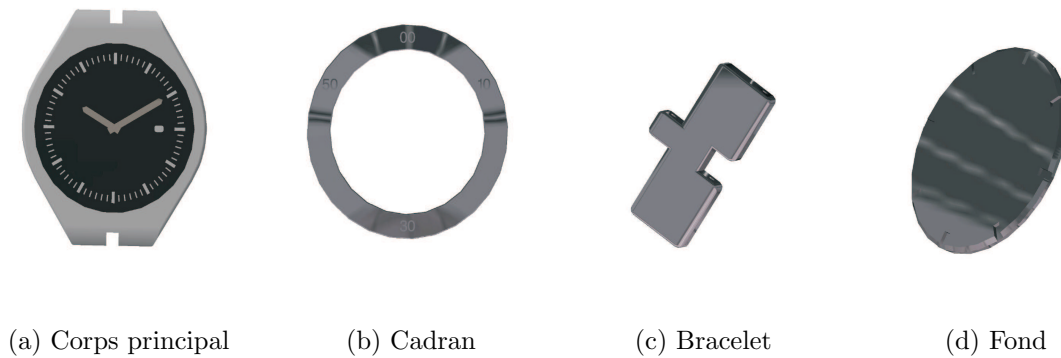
Pièces définissantes l'assemblage de la montre M_{19}
